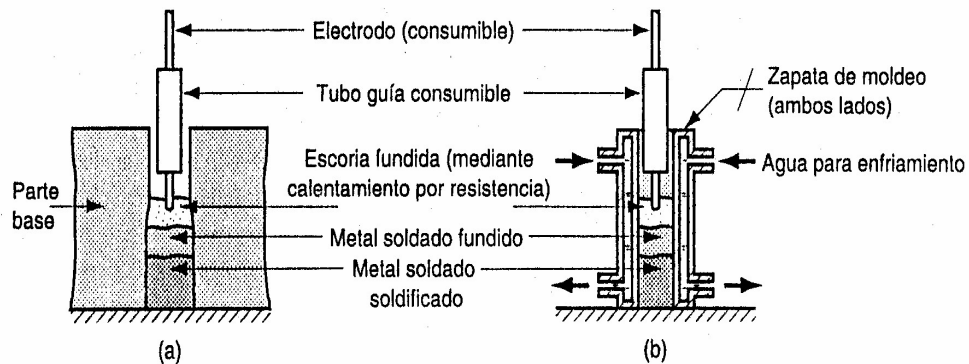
Soldadura con electro escoria (ESW): (a) vista frontal con zapatas de moldeo removidas para mayor claridad y (b) vista lateral que muestra una esquema de la zapata de moldeo. La preparación es similar a la de soldadura electro gaseosa (figura 4.41), excepto que se usa el calentamiento por resistencia de escoria fundida para derretir los metales base y de aporte.
